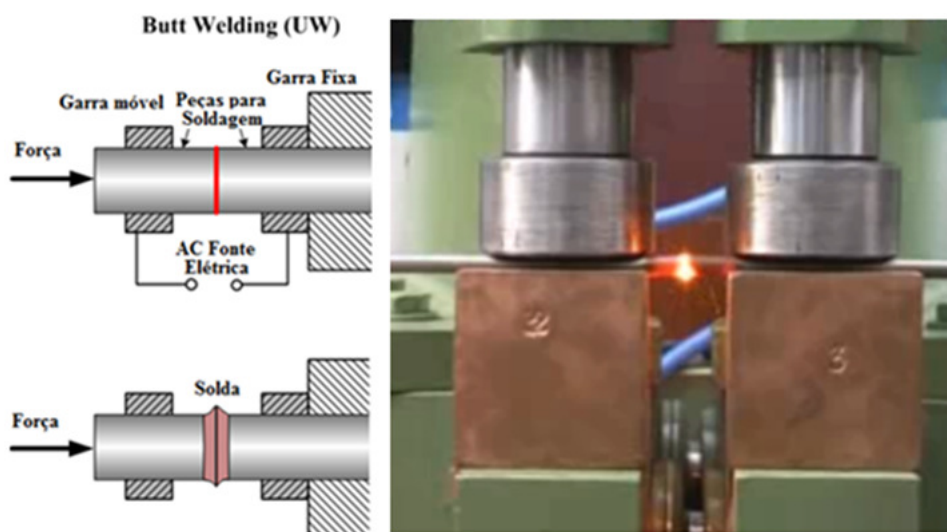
Exemplo da solda por resistência *Butt Welding* <sup>(12),(14)</sup>.
